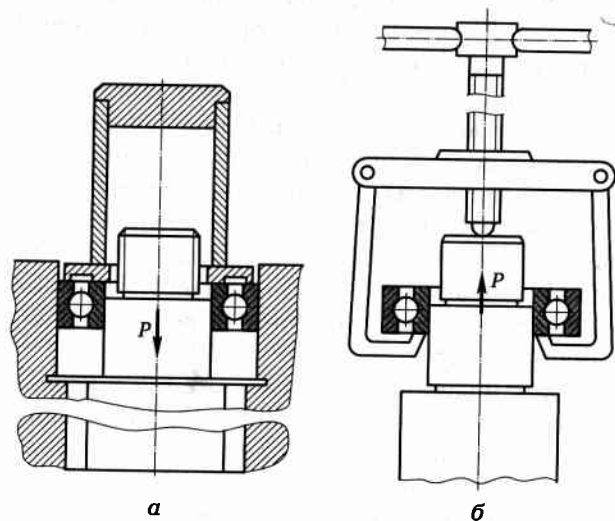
Приспособления для напрессовки (а) и снятия (б) подшипников:
